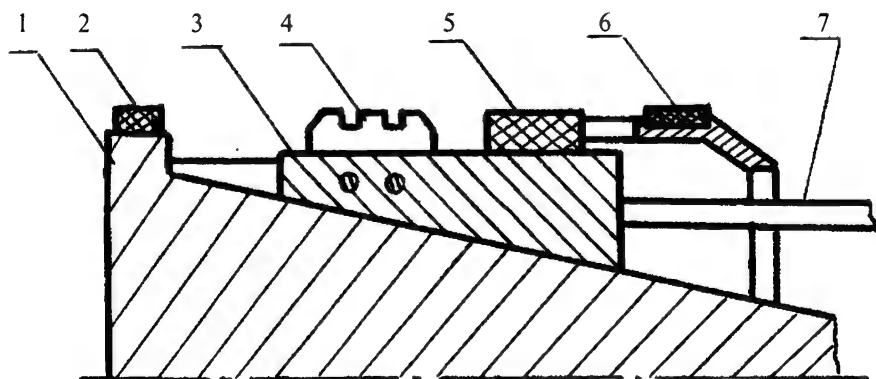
Приспособление с пазовым внутренним копиром: 1 - корпус, 2, 6 - неподвижные направляющие шпонки, 3 - колодка резцовая, 4 - резец, 5 - подвижная направляющая, 7 - тяга
